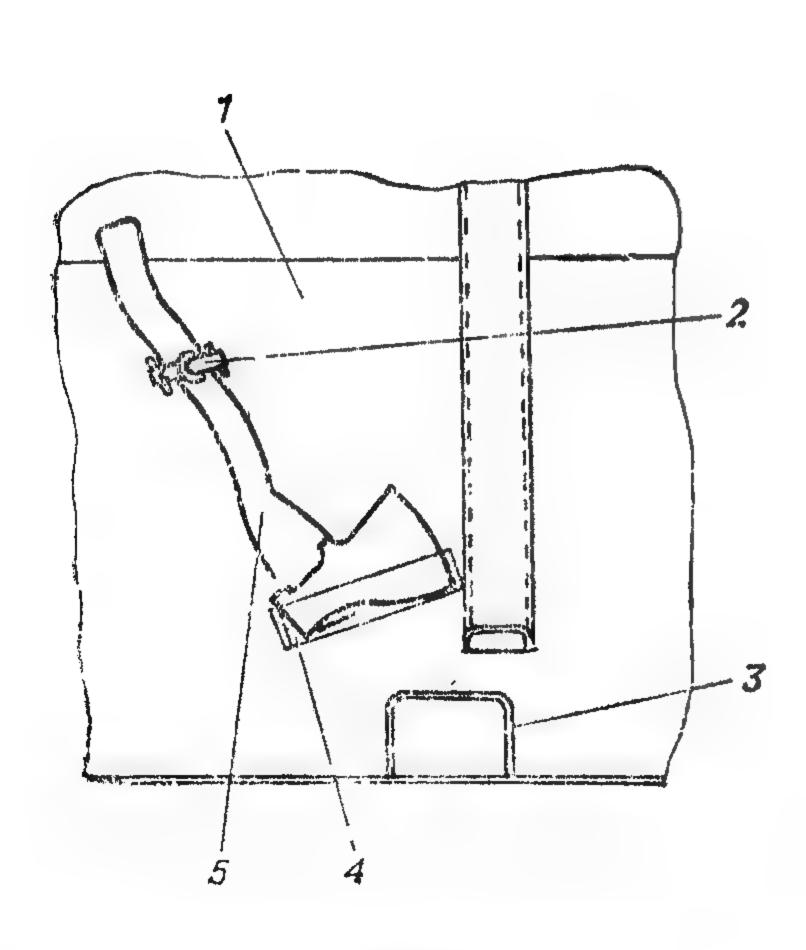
Установка топора: 1 — борт правый нижний; 2 — ремень; 3 — балка торсионная; 4 — упор; 5 — топор
